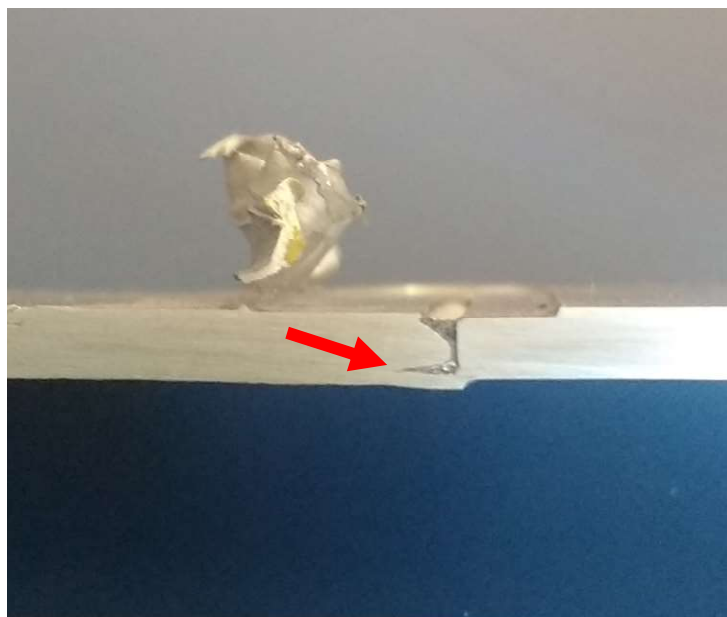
Junta soldada de alumínio 5052 H34 com canal retangular
